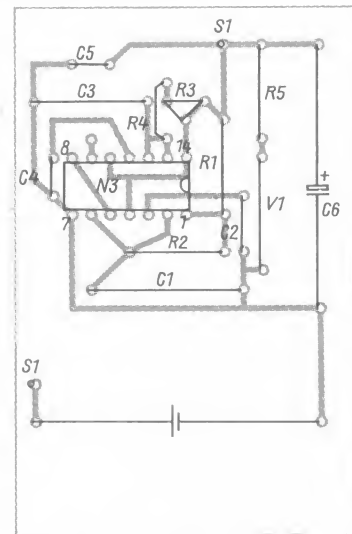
Bestückungsplan zu Schaltungsvariante 2
